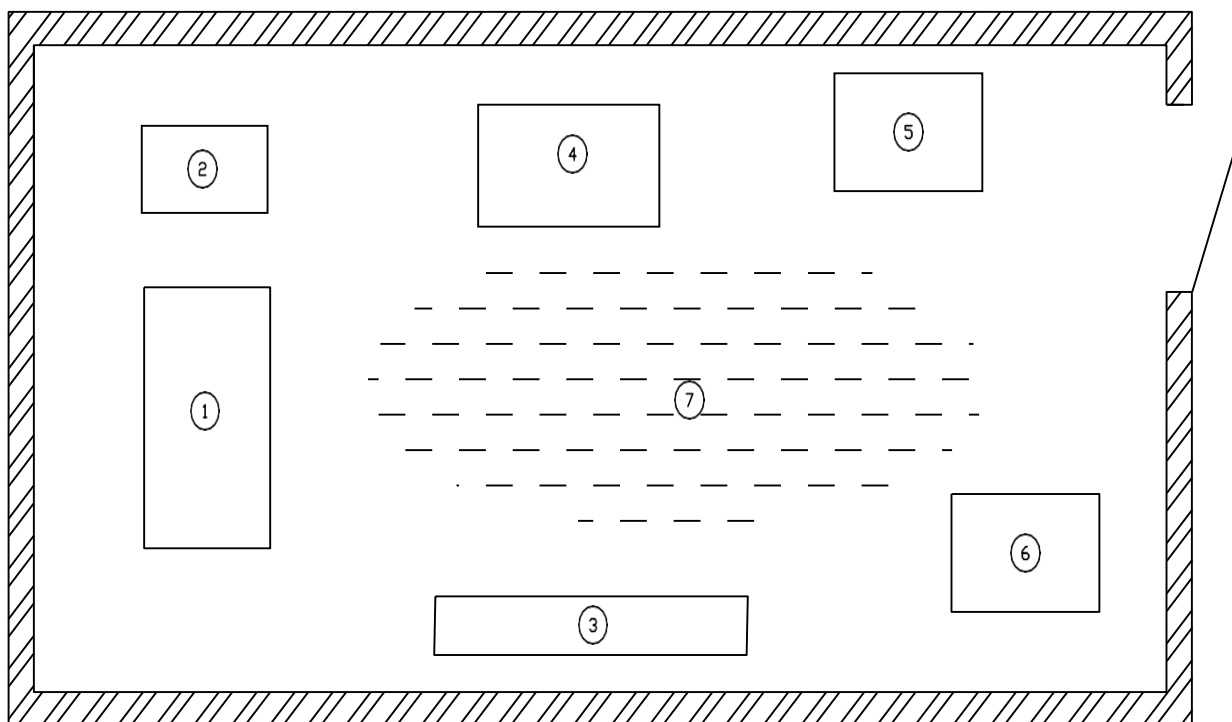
Расположение оборудования в сварочной мастерской
